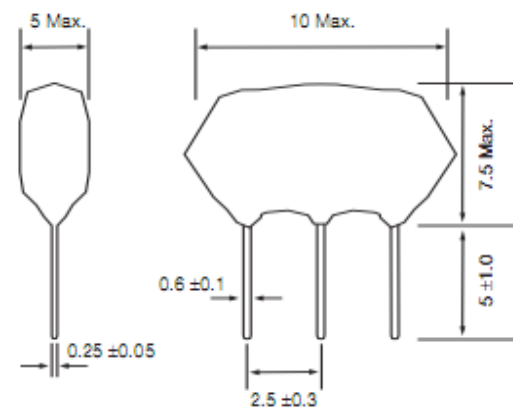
Кварцовий резонатор ZTT 10МГц
